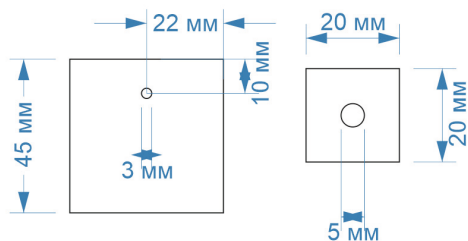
Чертеж для выпиливания деталей из инструкции по сборке «Настольный хоккей»
